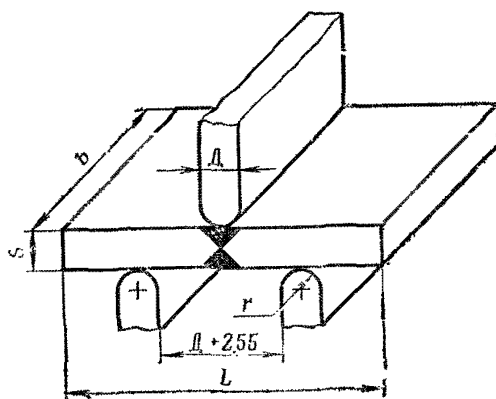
Схема испытания сварного шва на загиб. Образец типа, представленного на рис. 4
